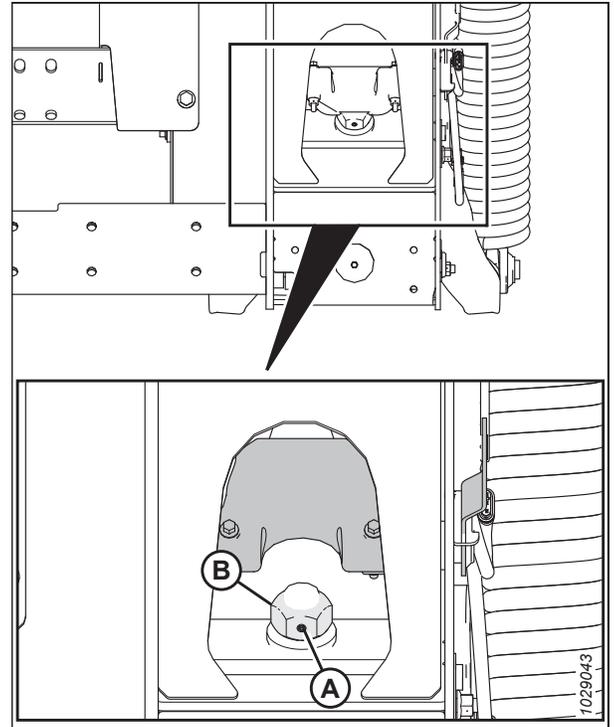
Dispositivo di bloccaggio flottazione – Destra
